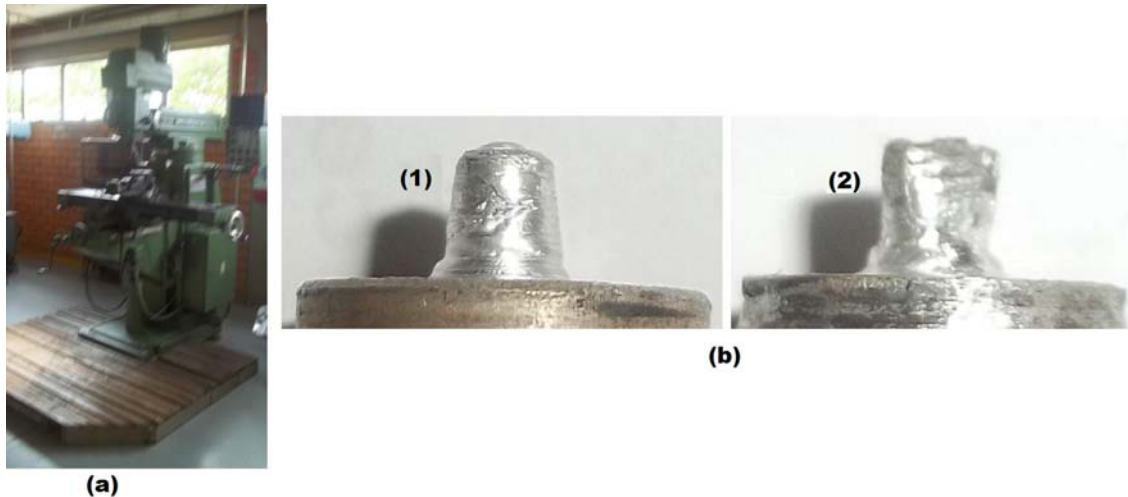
(a) Fresadora universal utilizada para o processo FSW; (b) ferramentas projetadas e fabricadas para a soldagem FSW.
